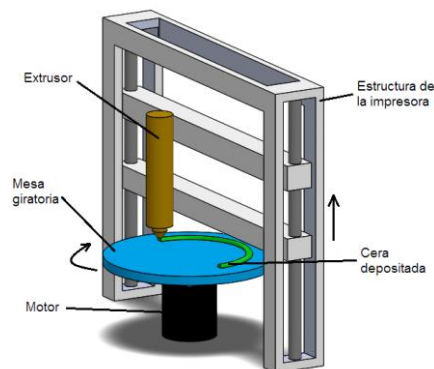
Esquema del montaje para la prueba de impresión.
